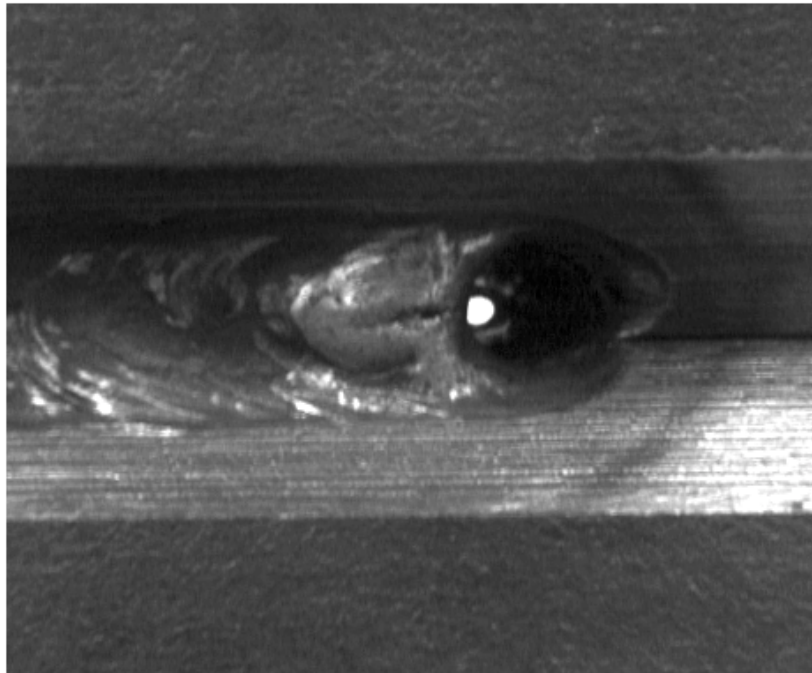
Aspecto do “keyhole” na parte final do cordão de solda.
